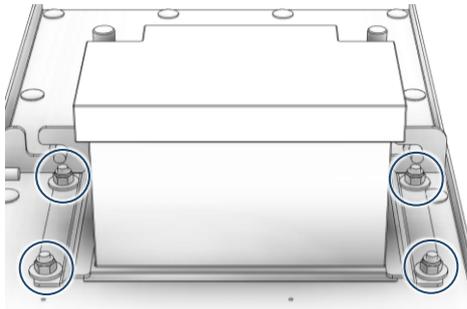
Entfernen der Befestigungsmuttern der Profile
